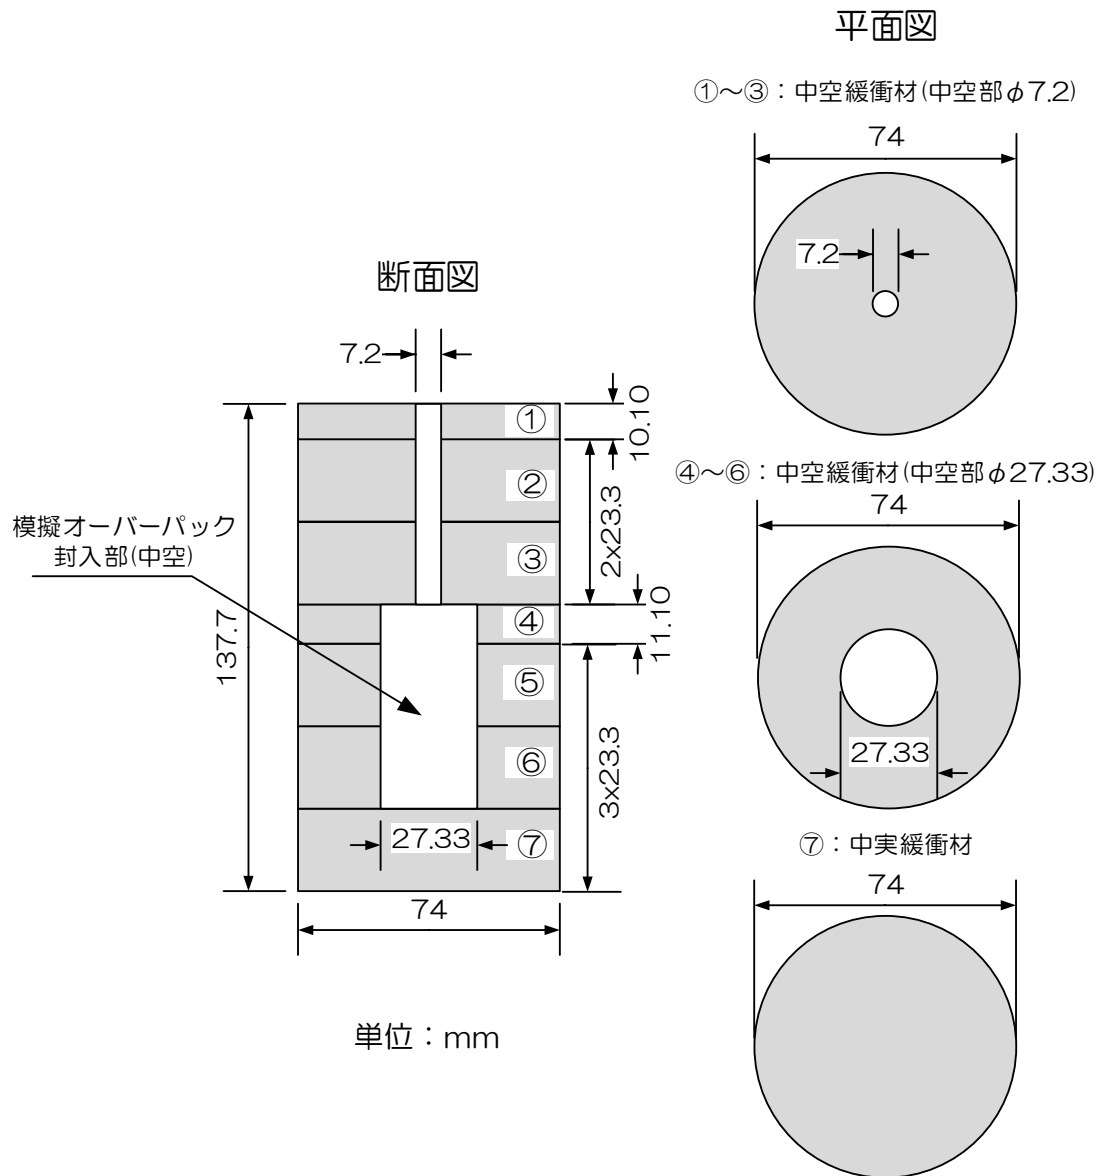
緩衝材ブロックの断面図、平面図および分割状況
